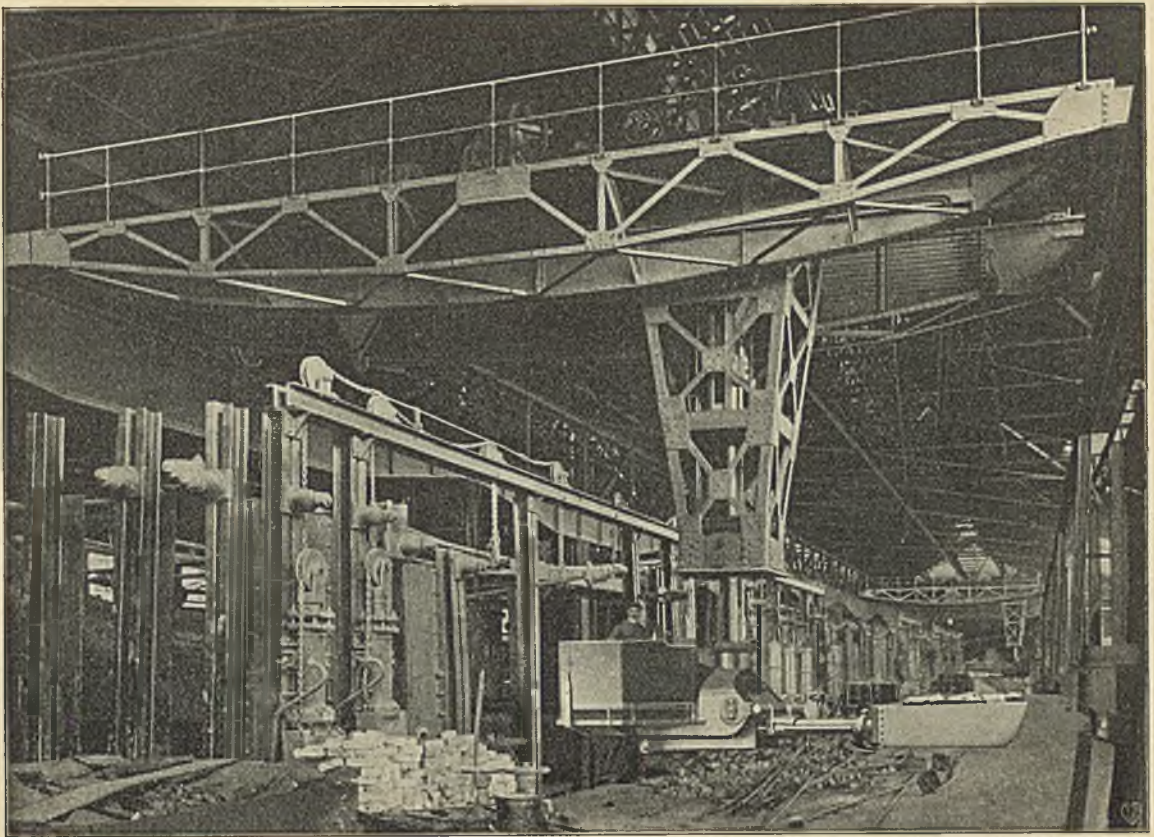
Elektrisch betriebene Muldenchargiermaschine mit 7 Motoren.
